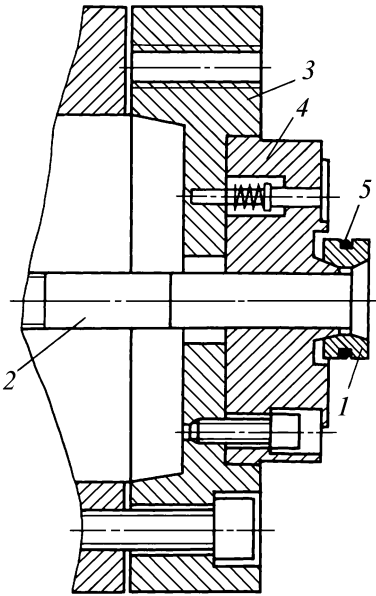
Разжимной патрон для крепления тонкостенных заготовок:
